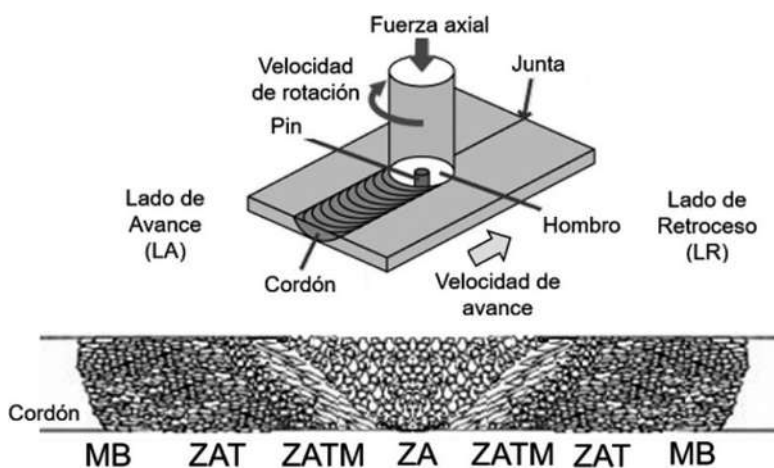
Zonas características de la soldadura por FSW. [33]
